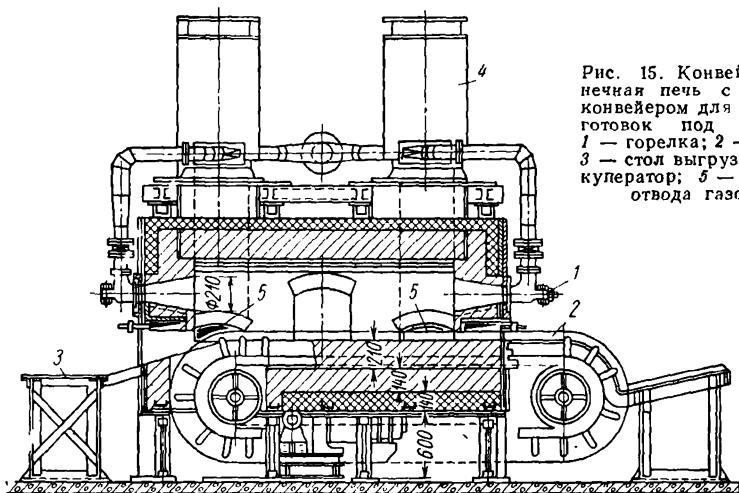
Конвейерная кузнечная печь с подподовым конвейером для нагрева заготовок под штамповку: 1 — горелка; 2 — конвейер; 3 — стол выгрузки; 4 — рекуператор; 5 — каналы для отвода газов [13]
